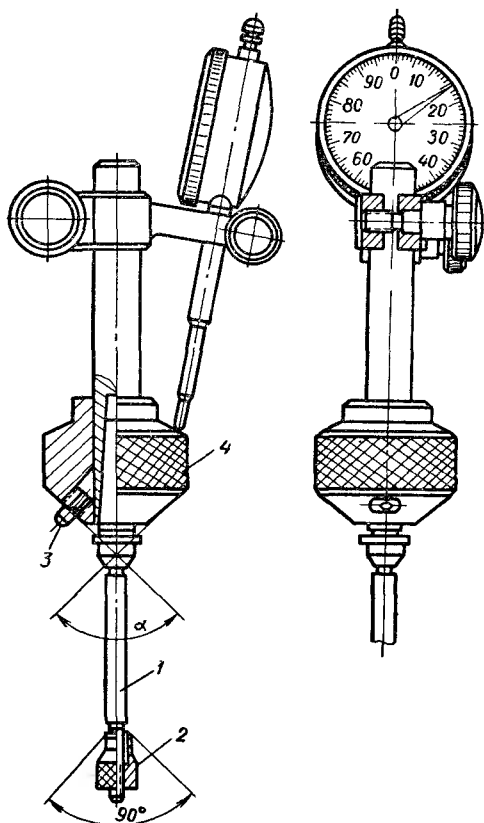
Приспособление для контроля concentricности седла клапана относительно отверстия в головке под стержень клапана
